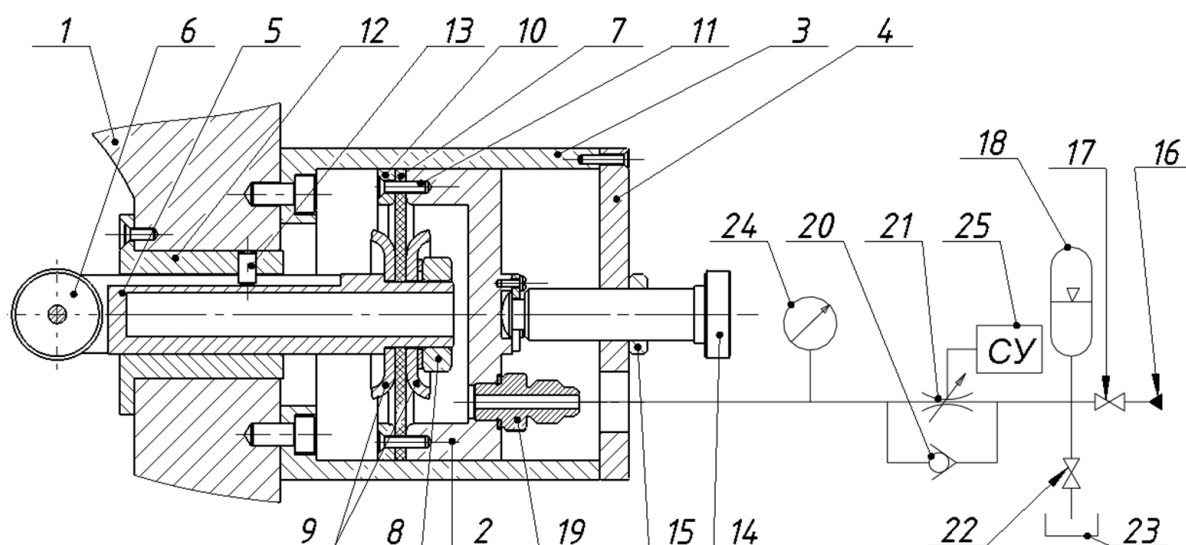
Рабочий узел виброгасителя вязкого трения: 1) стойка; 2) гидроцилиндр; 3) стакан; 4) крышка; 5) плунжер; 6) ролик; 7) диафрагма; 8) гайка; 9) сферическая шайба; 10) кольцо; 11) винт; 12) втулка направляющая; 13) штифт; 14) винт регулировочный; 15) контргайка; 16) источник давления; 17) вентиль; 18) пневмогидроаккумулятор; 19) штуцер; 20) обратный клапан; 21) дроссель; 22) вентиль; 23) гидравлический бак; 24) манометр; 25) система управления
